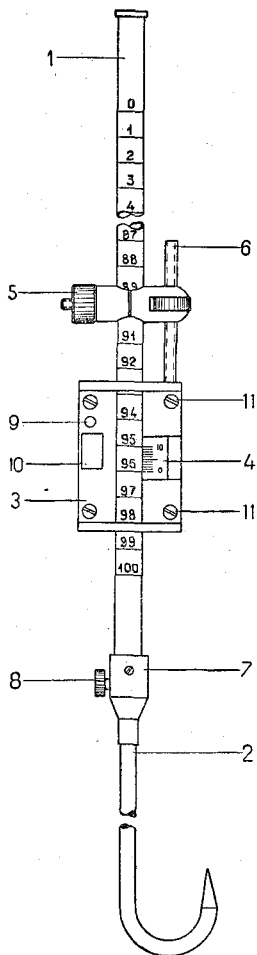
Приспособление для поверки реек крючковых и игольчатых.
